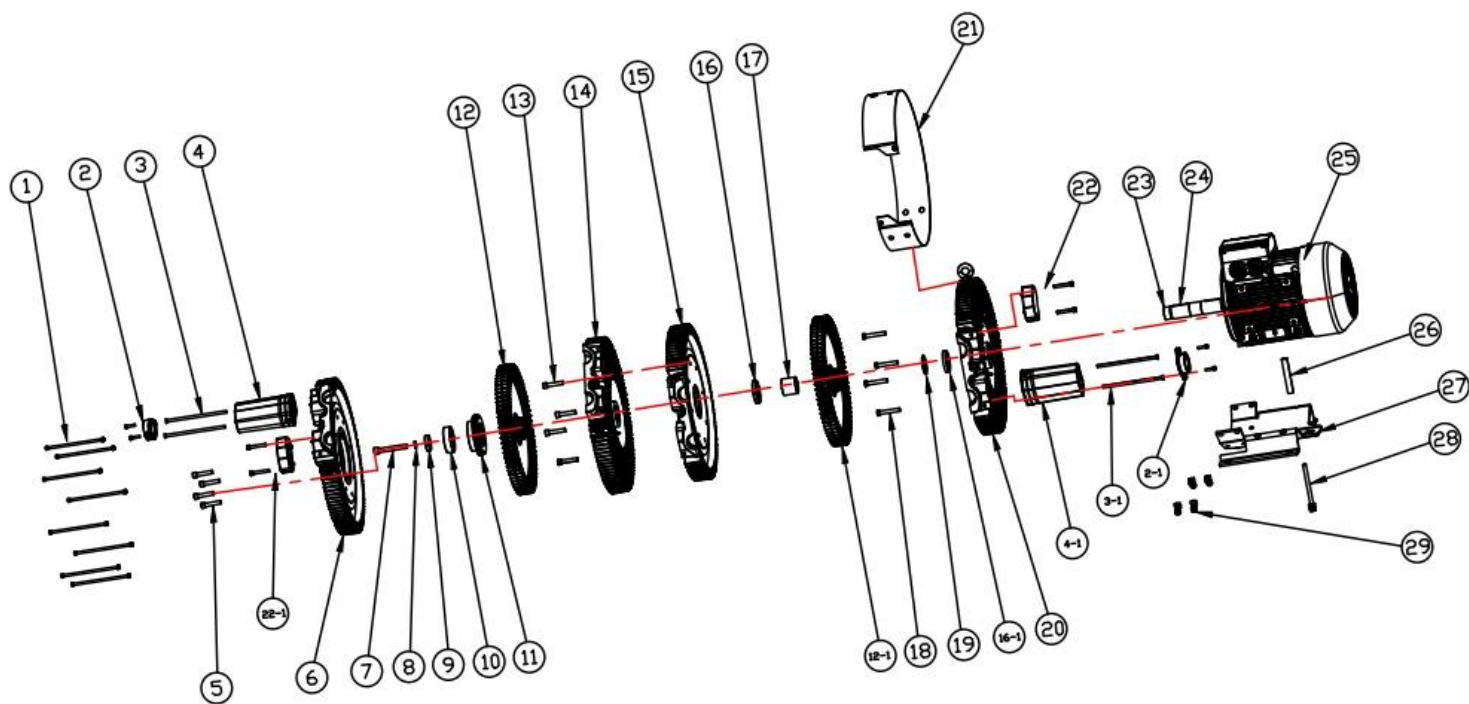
Деталировка двухступенчатых воздуходувок 4RB
